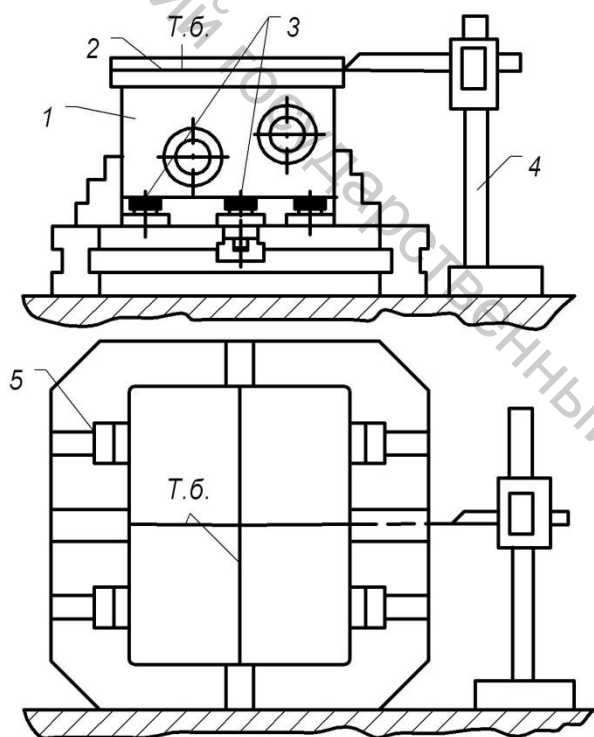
Реальное базирование заготовки в приспособлении-спутнике по разметке
